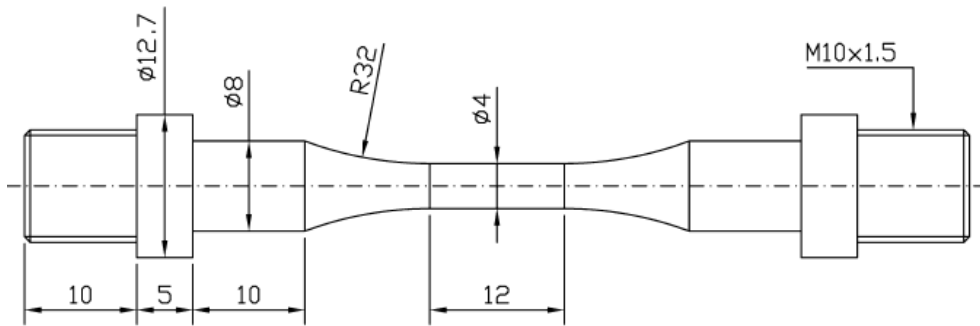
Dimensões corpos de prova usinados para ensaios de fadiga (mm).
